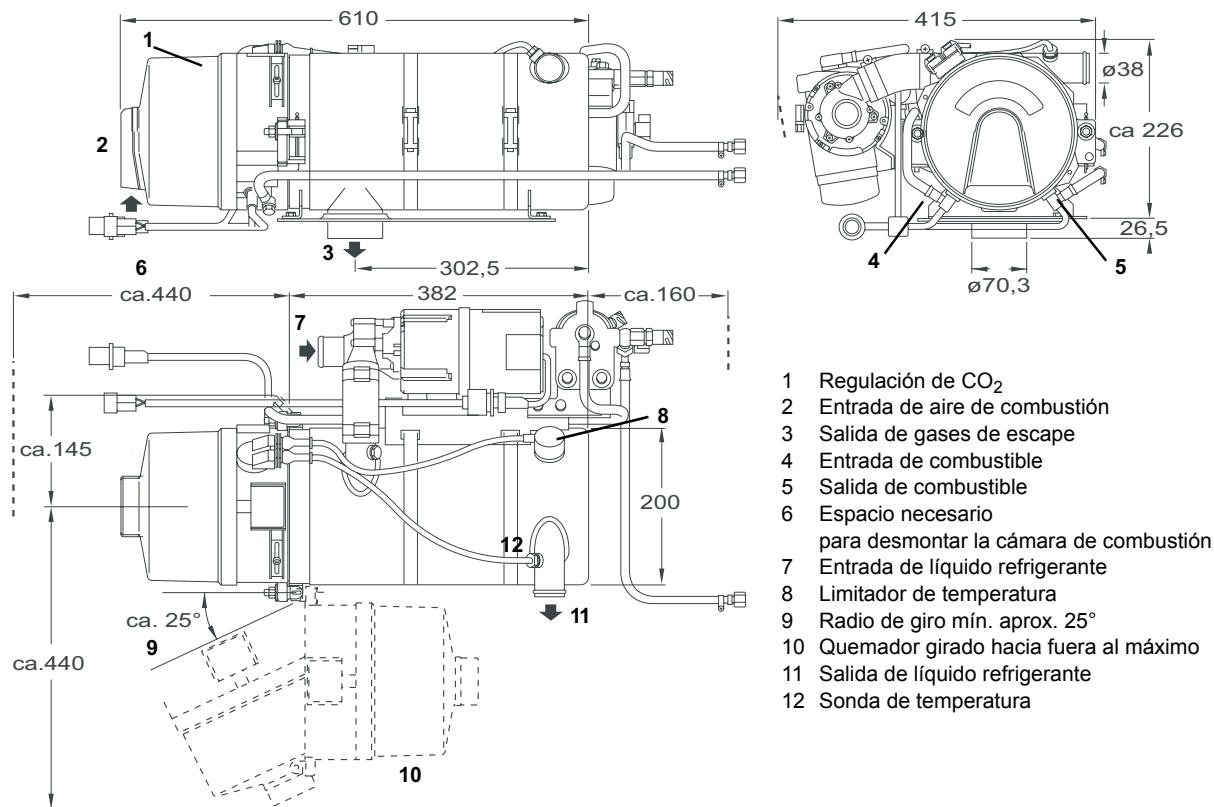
Dimensiones del calentador Thermo 230 / 300 / 350 Rail
